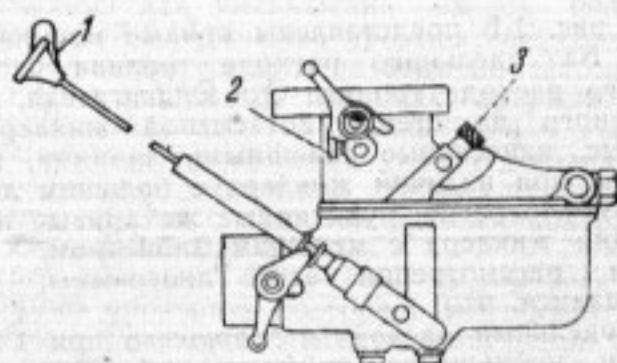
Схема регулировки карбюратора Форд-Зенит
